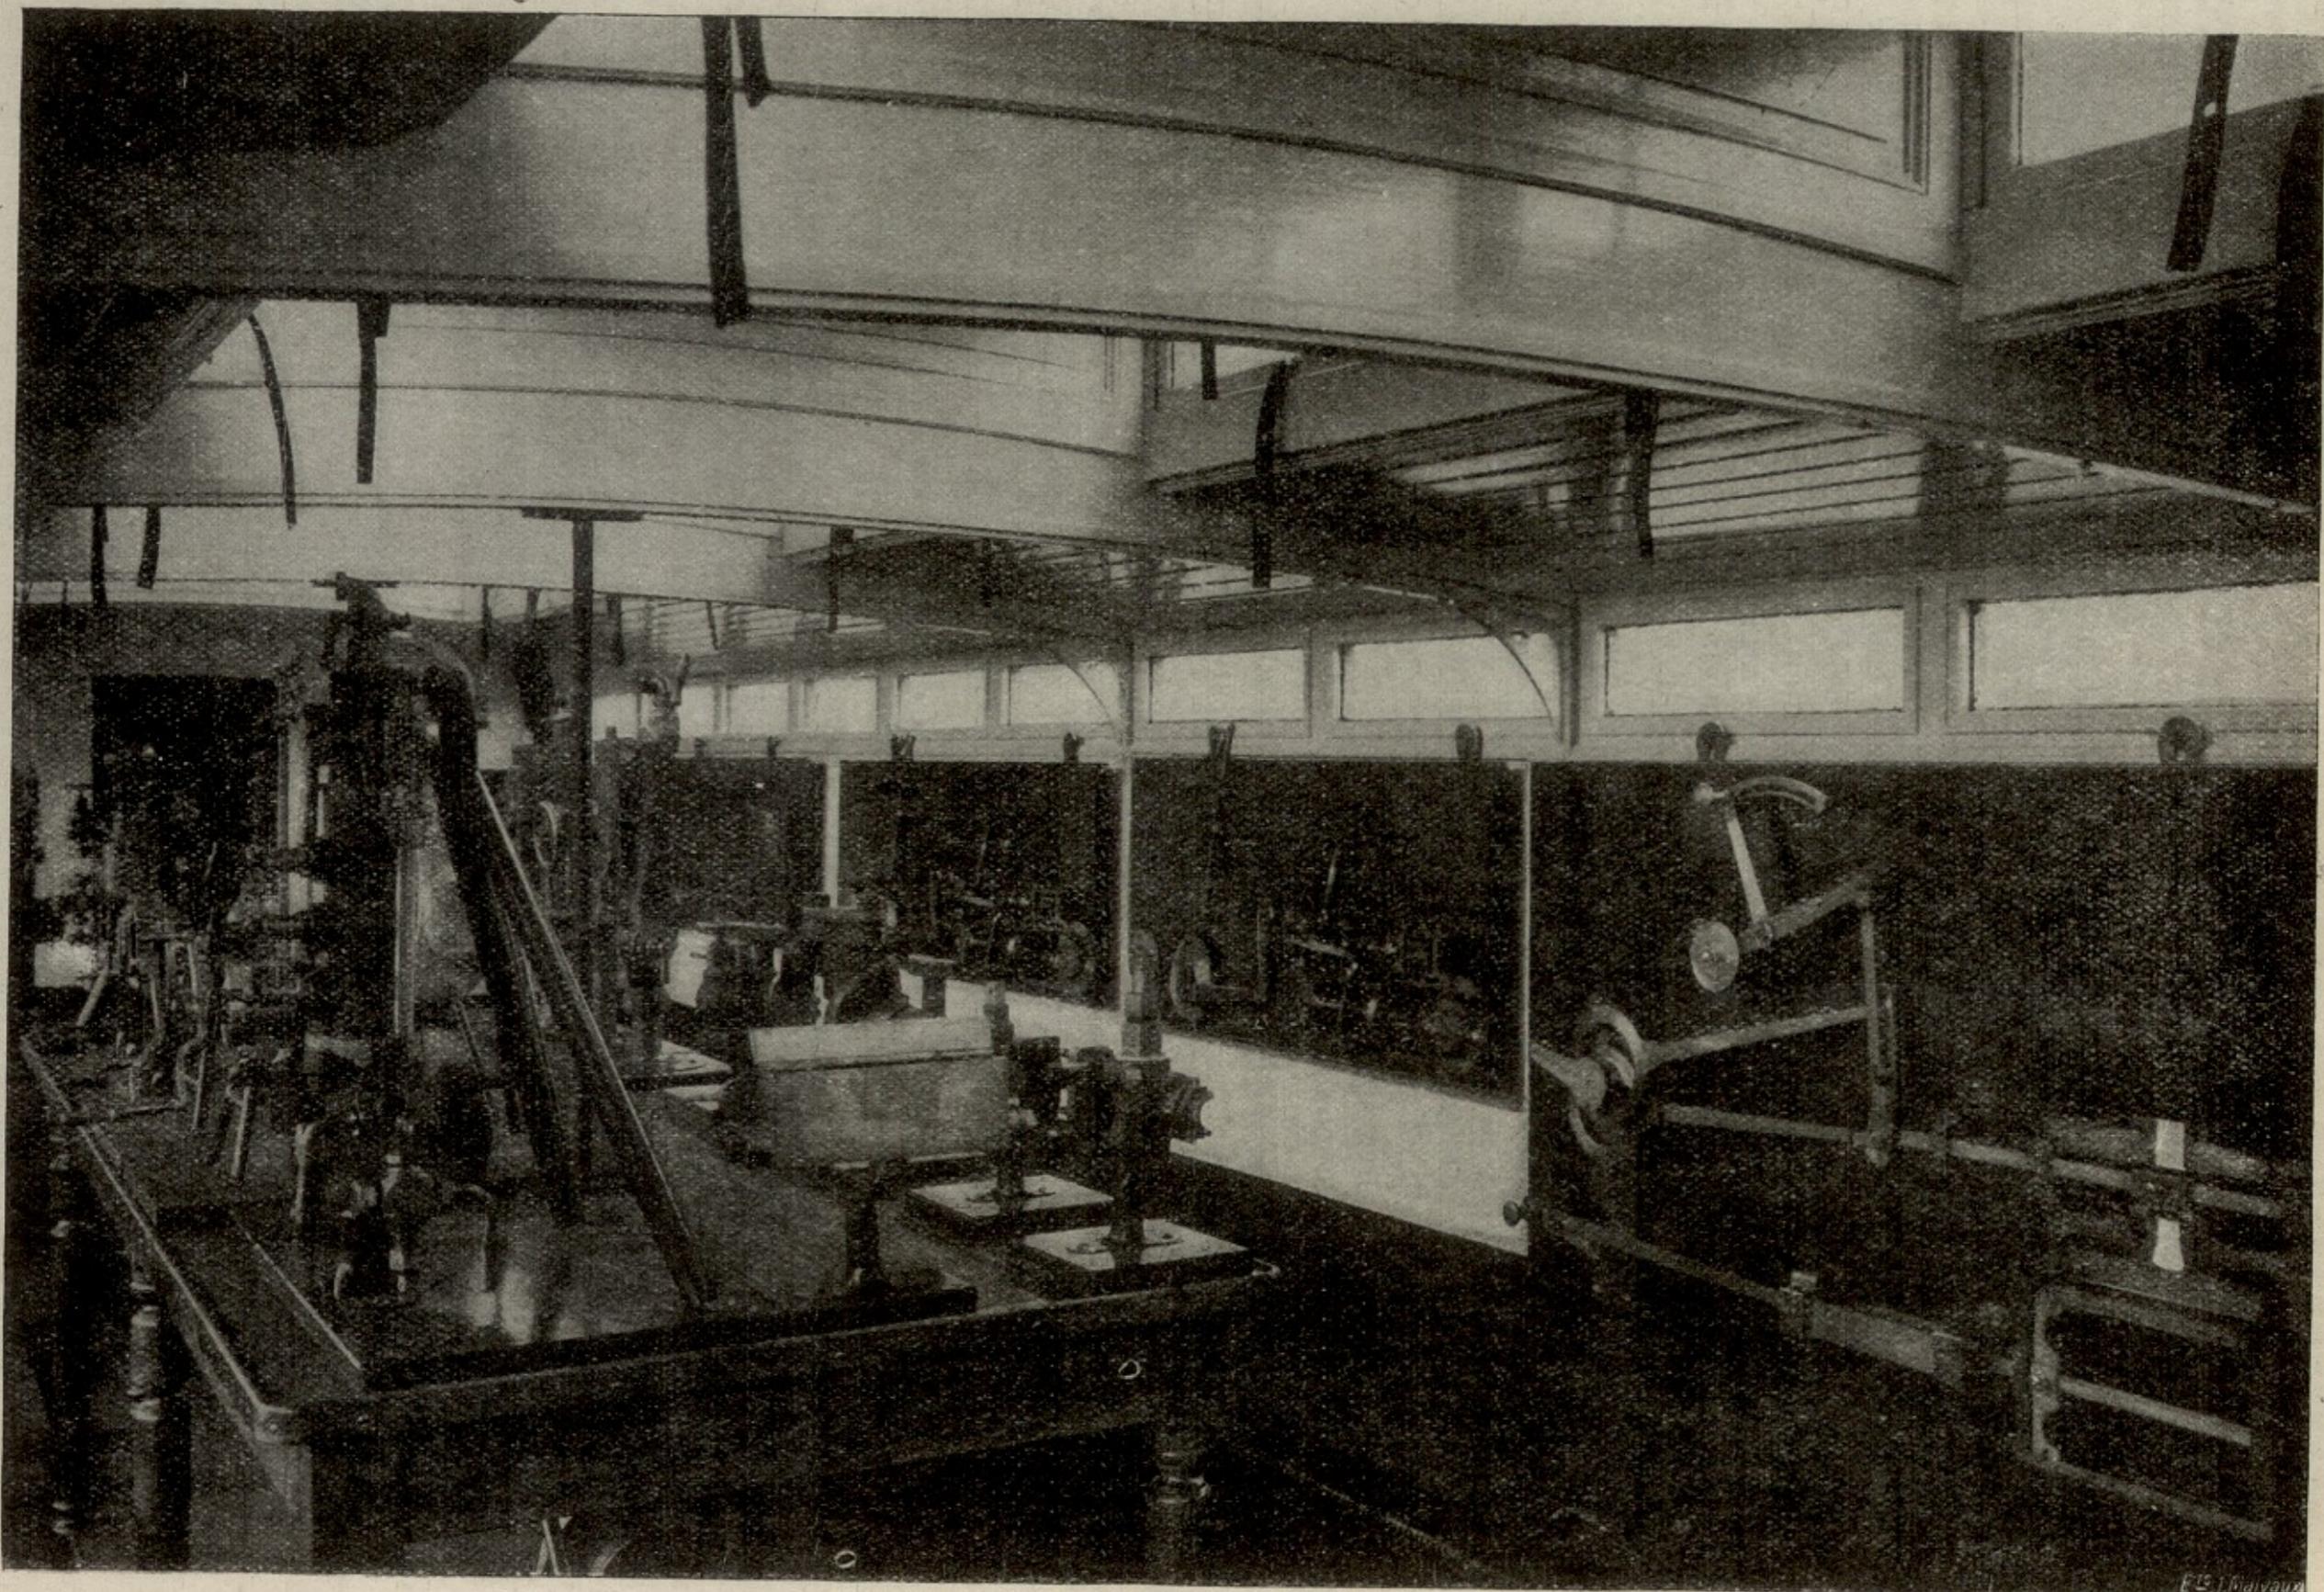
Vue d'ensemble de la salle de démonstration de la première usine.
